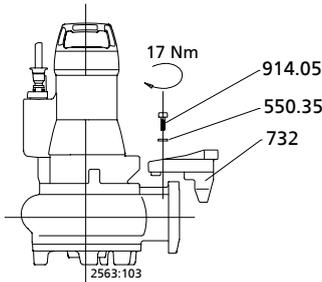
Montaggio del supporto per guida a fune, guida a 1 barra e guida a staffa
